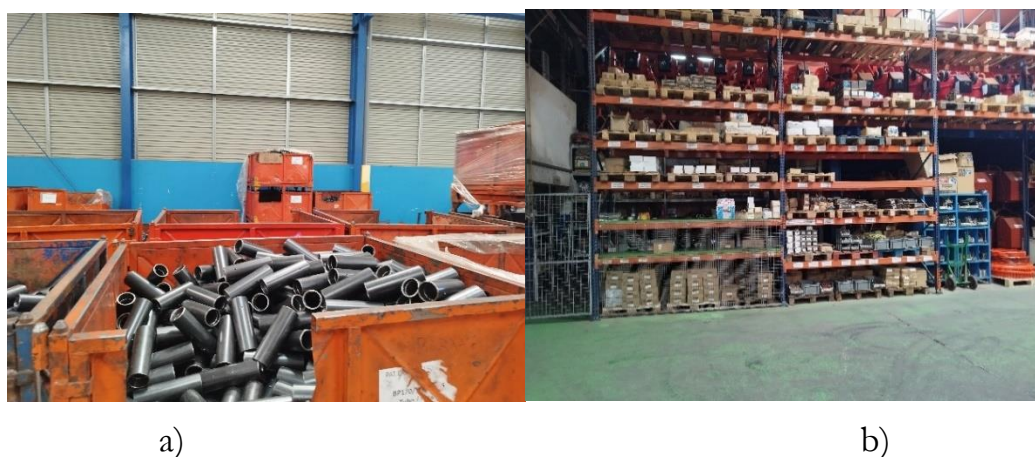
a) Componentes maquinados; b) Componentes elétricos.
